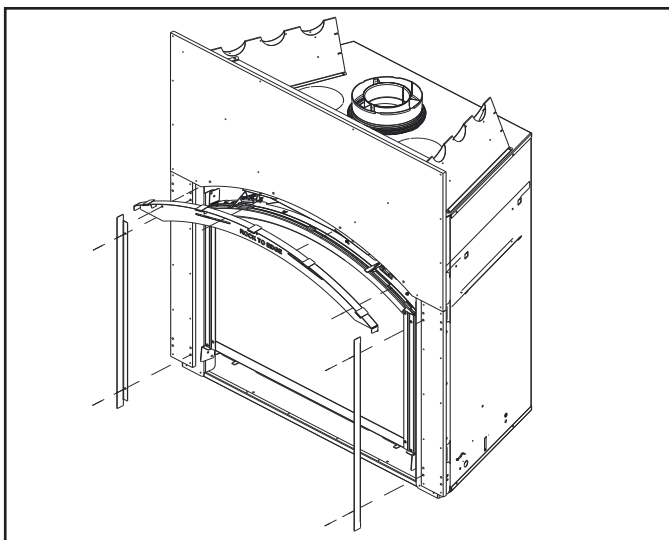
Pièces de finition du haut et de la voûte assemblées
